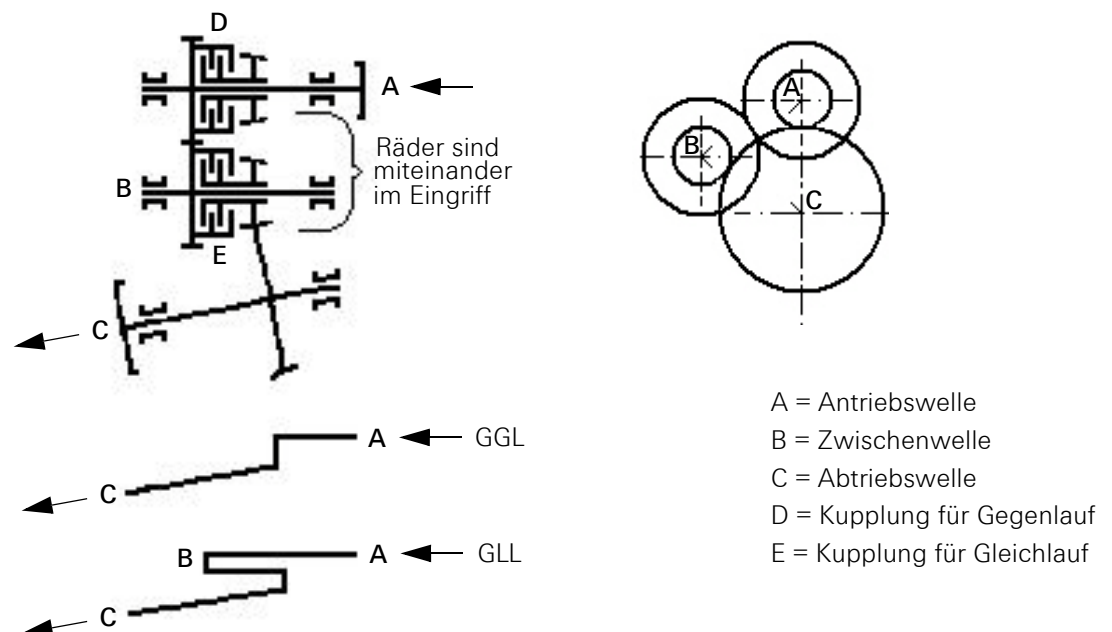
Kraftflussschema der A-Ausführung (Beispiel, GLL = Gleichlauf, GGL = Gegenlauf)
